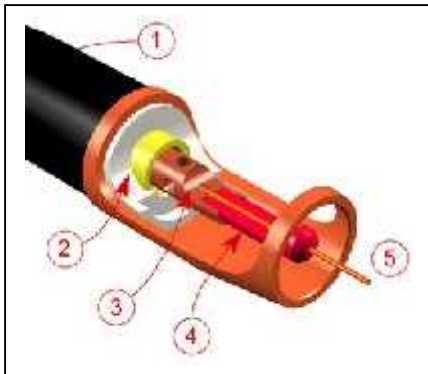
soudage semi-automatique (MIG/MAG)
